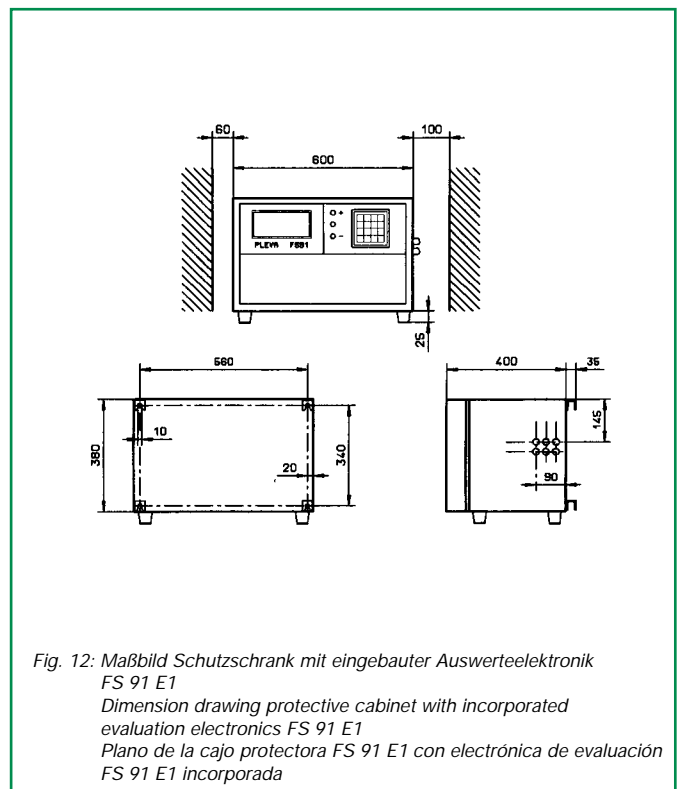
Maßbild Schutzenschrank mit eingebauter Auswerteelektronik
